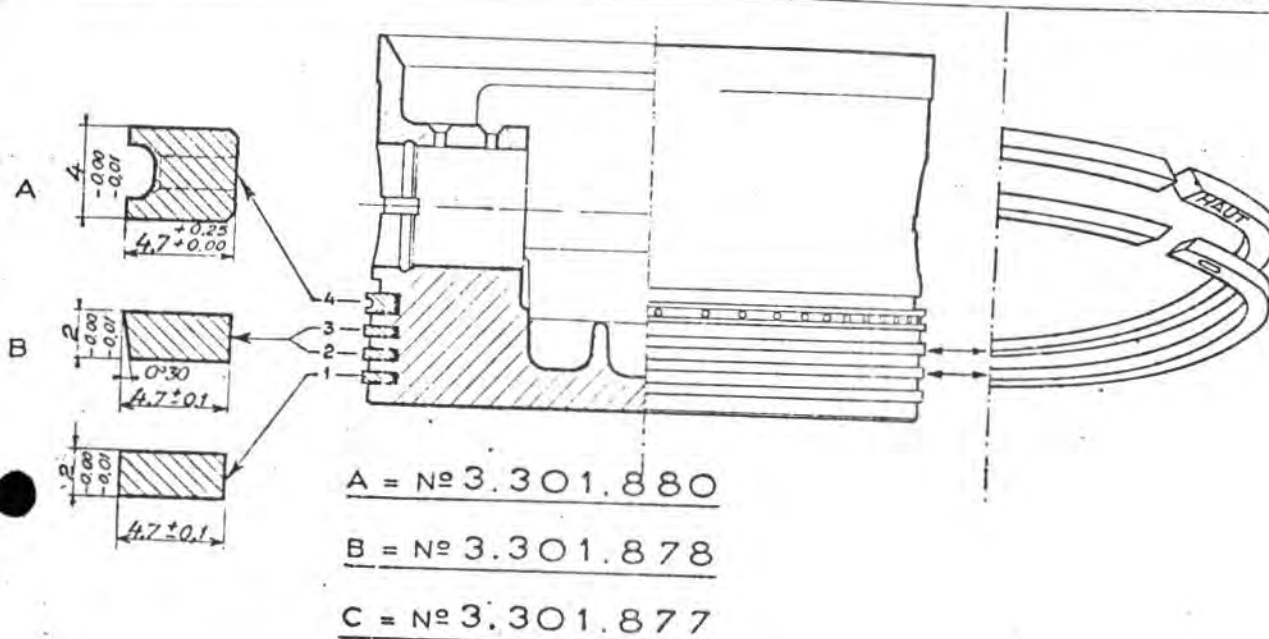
REPÉRAGE ET MONTAGE DES SEGMENTS.
